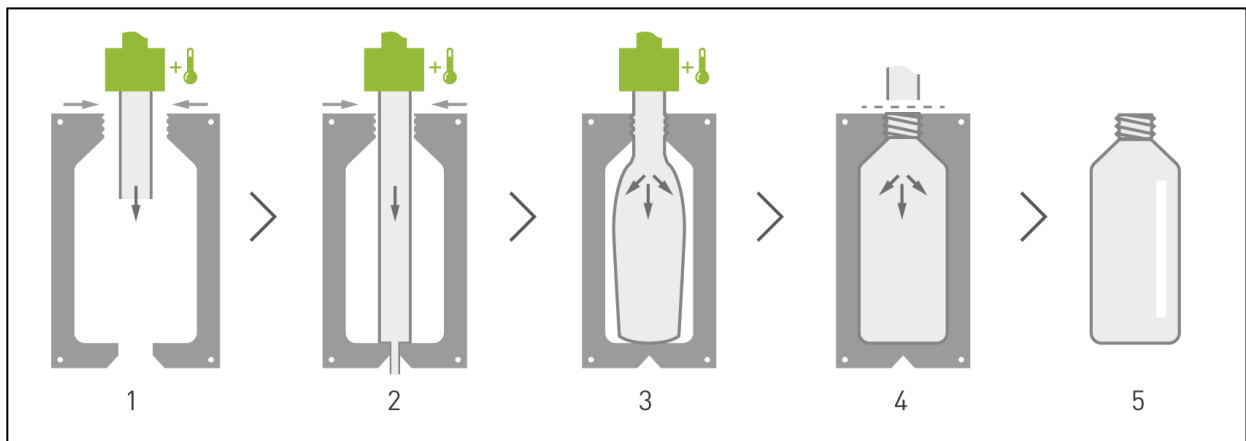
Proceso de Moldeo por Extrusión-Soplado
